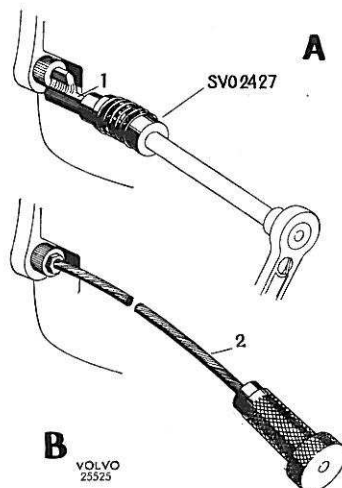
Démontage des vis de la boîte de vitesses, voitures équipées d'un moteur B 16
